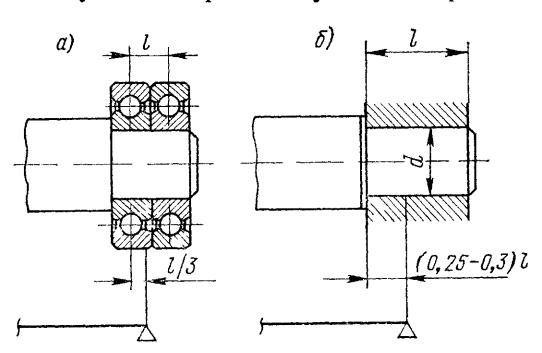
3 Длинные шарнирные опоры валов a — сдвоенные подшипники качения, δ — несамоустанавливающийся подшипник скольжения
